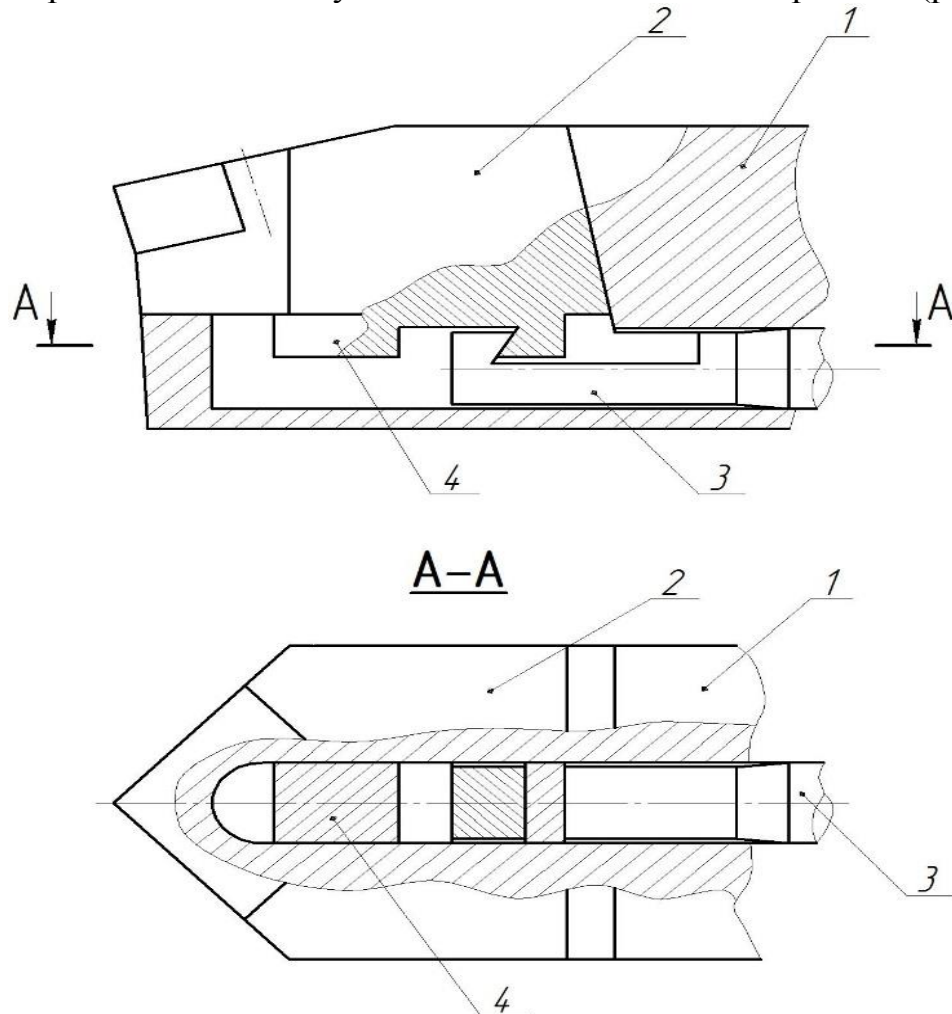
Конструкція вузла кріплення вставки до державки різця з прямокутним виступом на опорній поверхні: 1 – державка різця, 2 – різцева вставка з БНП, 3 – шток, 4 прямокутний напрямний виступ
